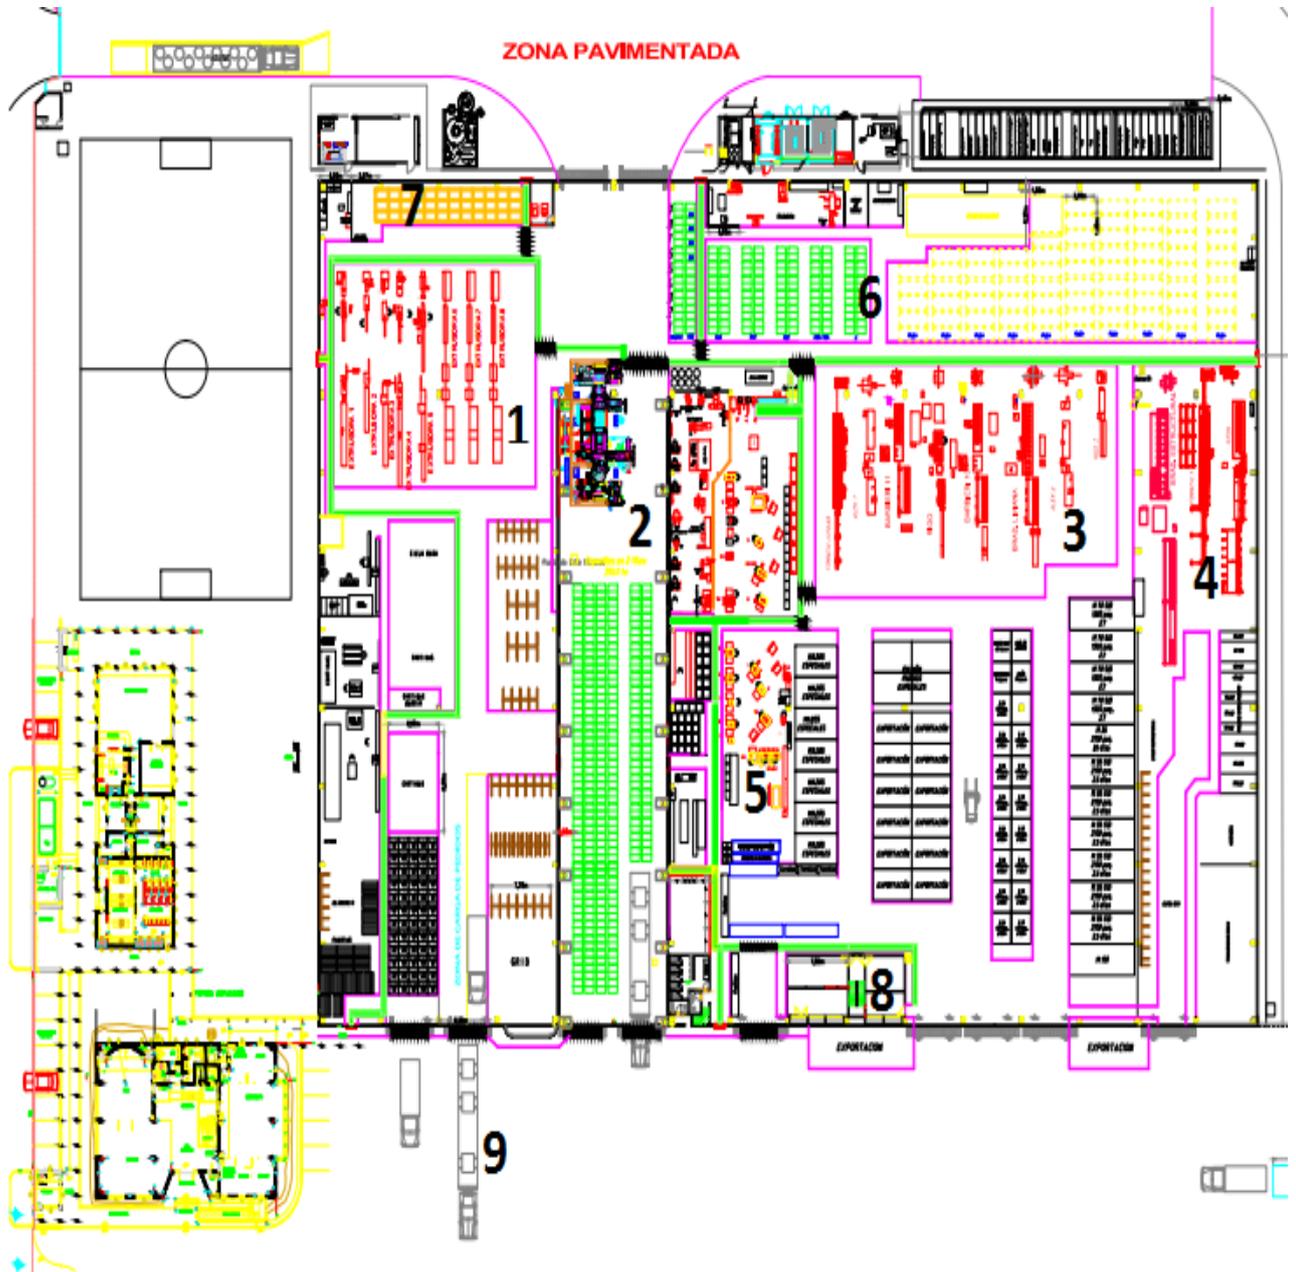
Lay Out actual de la planta industrial. Fuente: Barbieri SA
